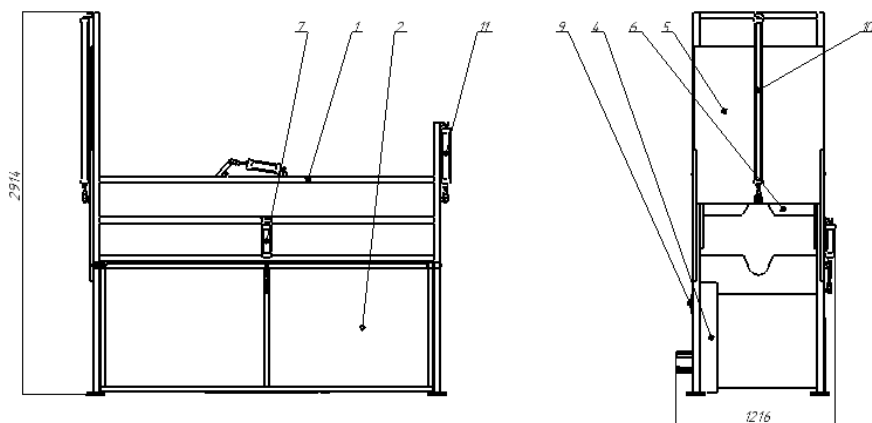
Общий вид бокса: 1 – каркас; 2, 3, 4, 5, 6 – дверь; 7, 8, 9, 10, 11 – пневмоцилиндр
